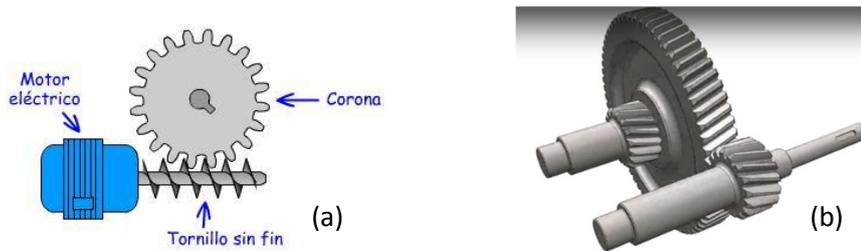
Reductor de velocidad de (a) tipo tornillo sin fin (b) tipo engranaje clásico
